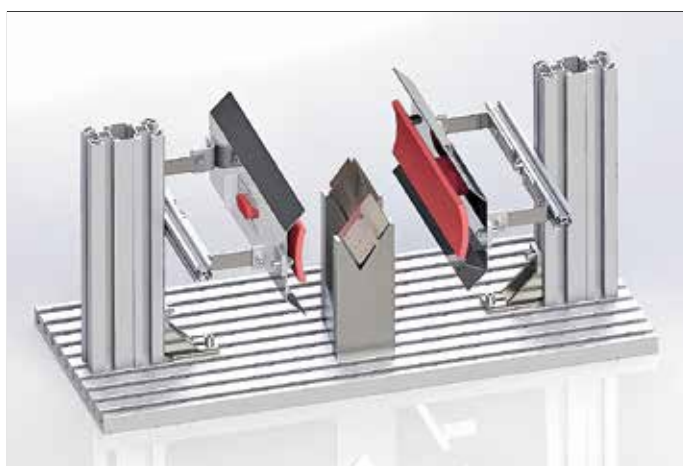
Модель оснастки для предварительного и сопутствующего подогрева лопатки
